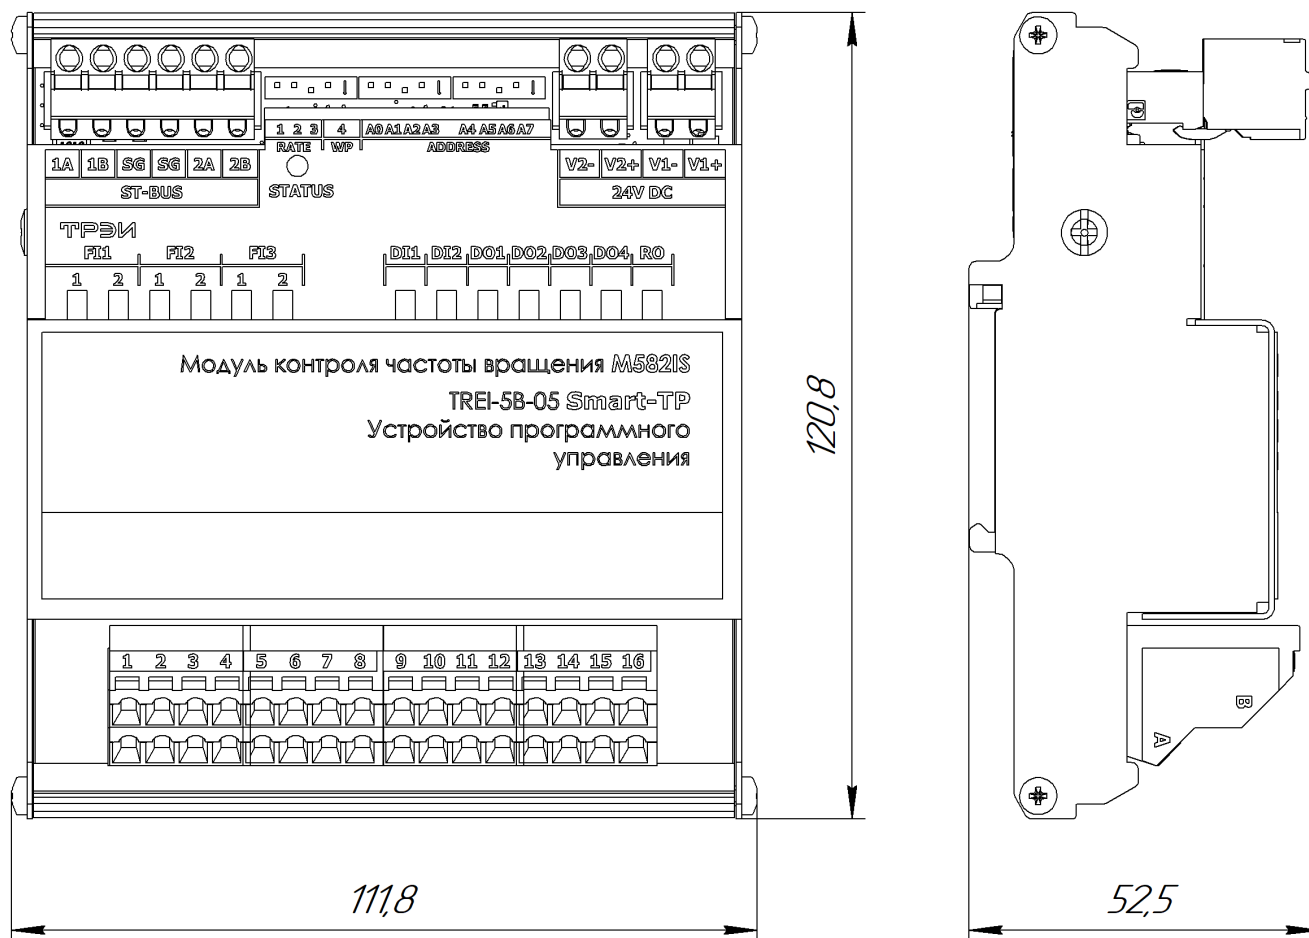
Чертеж общего вида M582IS с указанием габаритных и присоединительных размеров
